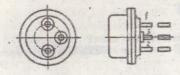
Общий вид и схема расположения выволов: 1 - эмиттер; 2 - коллектор; 3 - база
